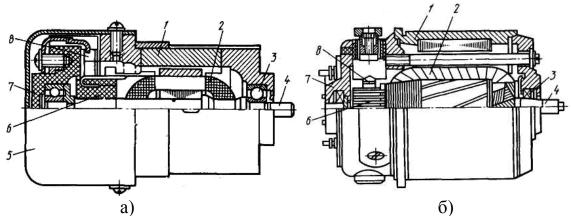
Устройство тахогенератора постоянного тока: а) с постоянными магнитами; б) с электромагнитным возбуждением 1 – корпус с полюсами; 2 – якорь; 3 – подшипник; 4 – вал; 5 – кожух; 6 – коллектор; 7 – подшипниковый щит; 8 – щетки.
